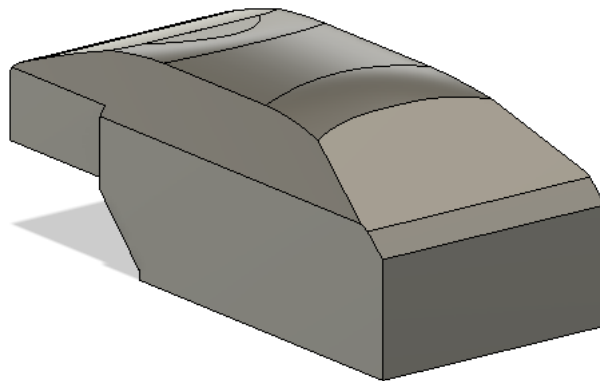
Modelo CAD de la cabina sin fotos de referencia.
